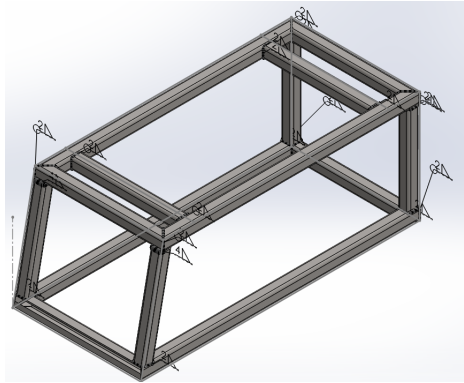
Perfiles cuadrado de 5/8 pulg. con uniones de soldadura.
